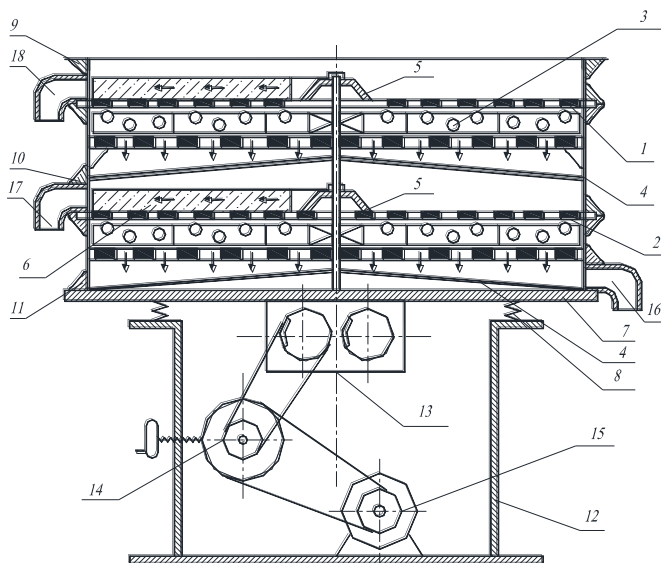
Конструктивна схема вібраційного сепаратора з перфорованим робочим органом: 1 – верхнє решето; 2 – нижнє решето; 3 – кульовий очисник решіт; 4 – конус розвантажувальний; 5 – конус натяжний з ділильником; 6 – планка ділильна; 7 – вібростіл; 8 – пружини; 9, 10, 11 – обечайки; 12 – станина; 13 – вібробудник; 14 – варіатор; 15 – електродвигун; 16, 17, 18 – розвантажувальні лотки
